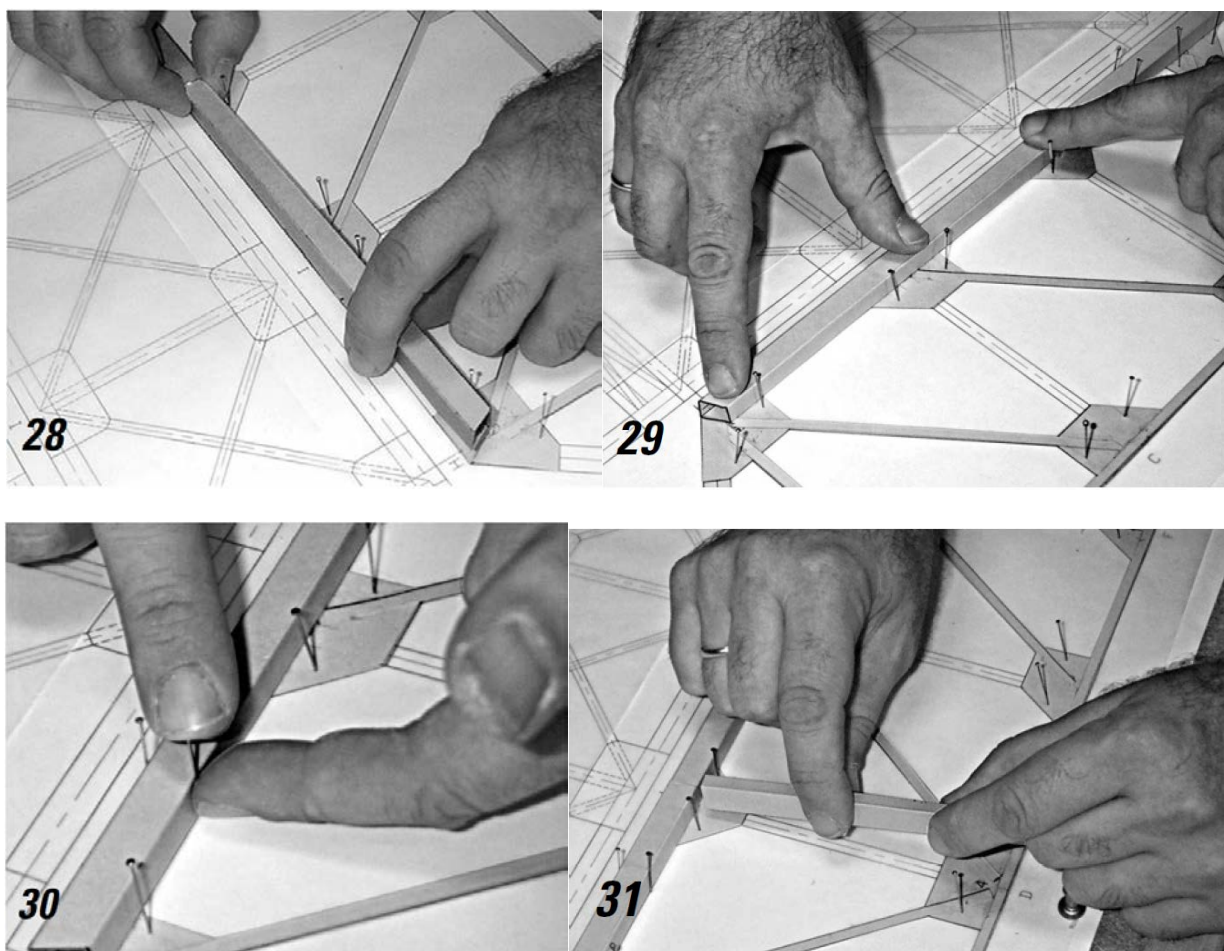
Montarea tălpilor și a montanților cu profil tip țeavă rectangulară
